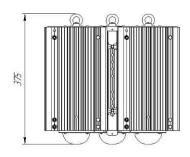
Габаритный чертеж светильника Econex Hell (240 70°C/120 100°C)
